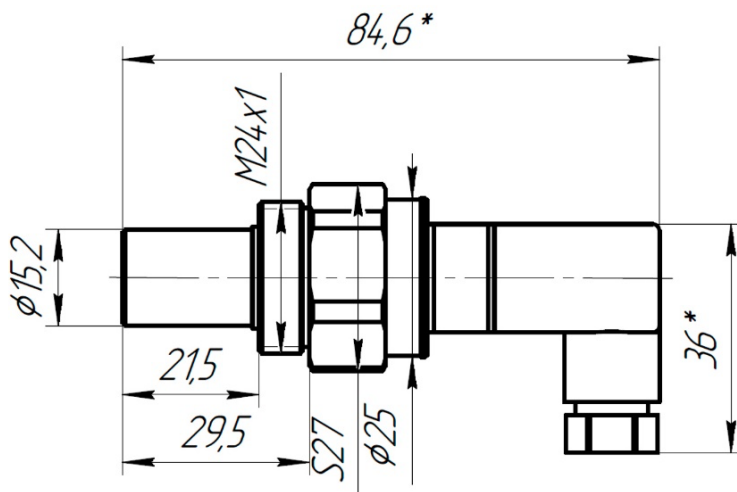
Установочные и габаритные размеры преобразователя ДВ2ТСМ-В.
